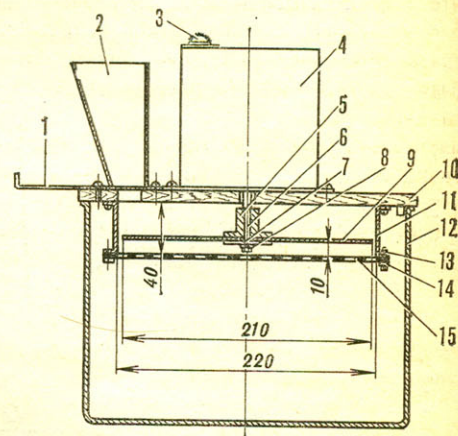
Конструкция дробилки: 1 — заслонка, 2 — бункер, 3 — выключатель электродвигателя, 4 — кожух электродвигателя, 5 — втулка, 6 — вал электродвигателя, 7 — шайба, 8 — гайка с пружинной шайбой, 9 — нож-пластина, 10 — основание, 11 — корпус рабочей камеры, 12 — бак, 13 — элементы резьбового крепления сетки, 14 — дугообразные прокладки, 15 — сетка.
